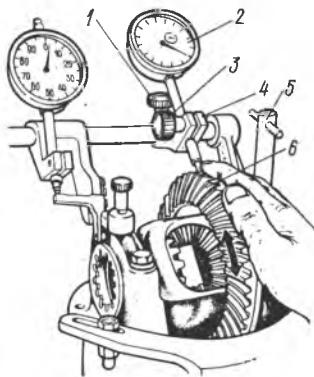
Проверка бокового зазора в зацеплении шестерен главной передачи приспособлением А 95688/Р:
